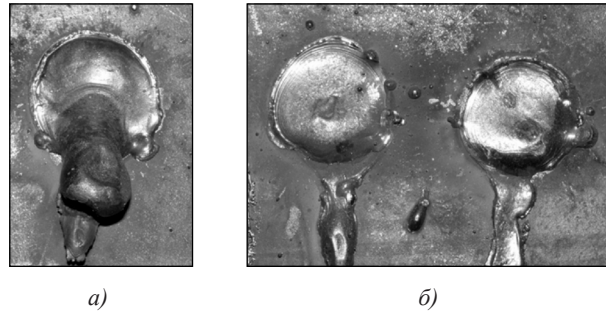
Зовнішній вигляд точкового з'єднання у вертикальному положенні: а — стікання розплавленого металу; б — неоднакове формування зварної точки
